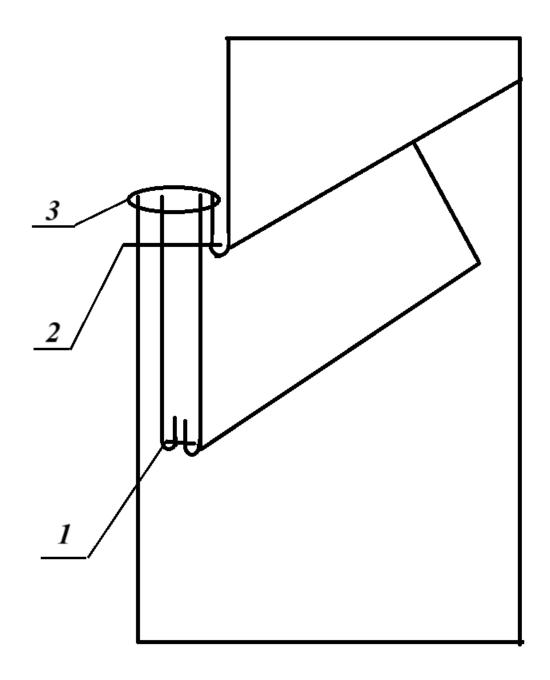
Схема обработки клапана в шве притачивания кокетки
